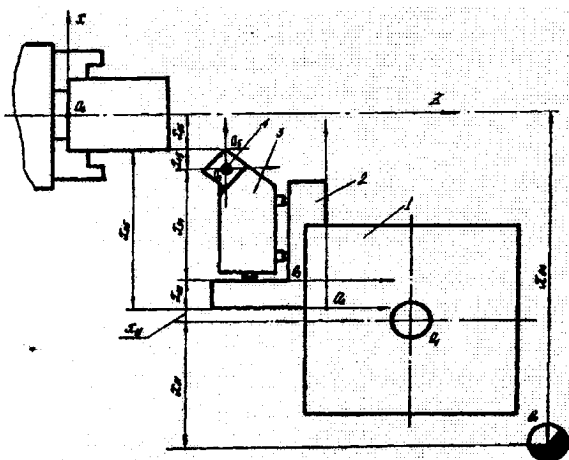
Безпідналагоджувальний інструмент в розмірному ланцюгу
